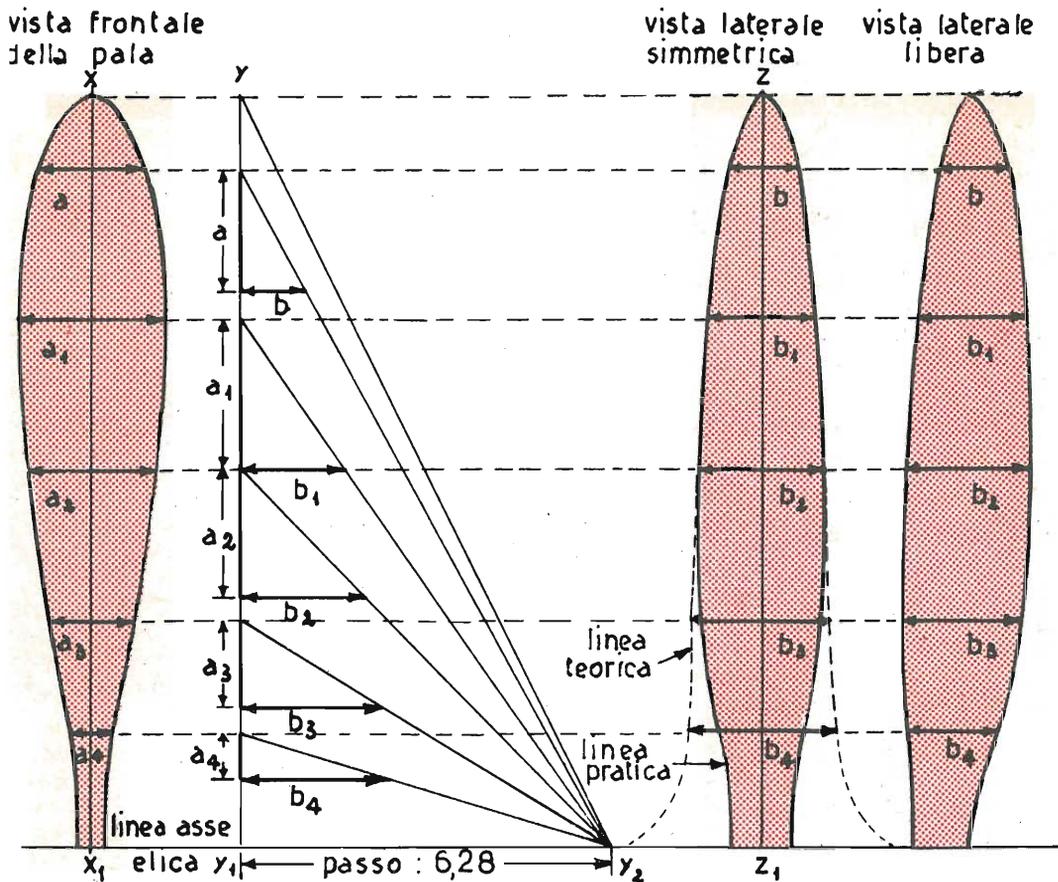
DISEGNO DELL'ELICA PARTENDO DALLA VISTA FRONTALE
